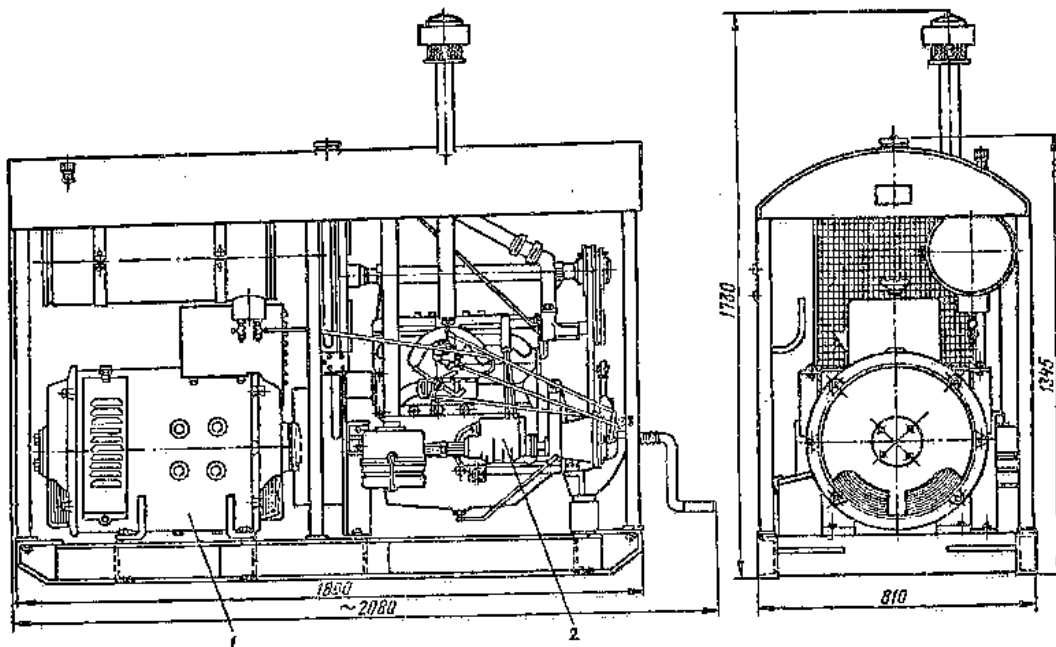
Схема конструктивного исполнения сварочного агрегата АСБ-300:
